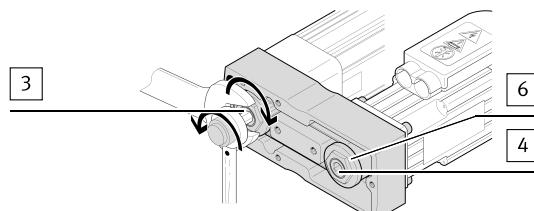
Затяжка до упора шкивов зубчатого ремня
